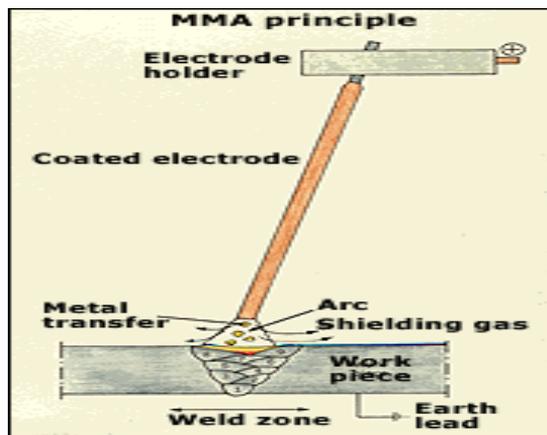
Esquema de soldadura por arco eléctrico.
